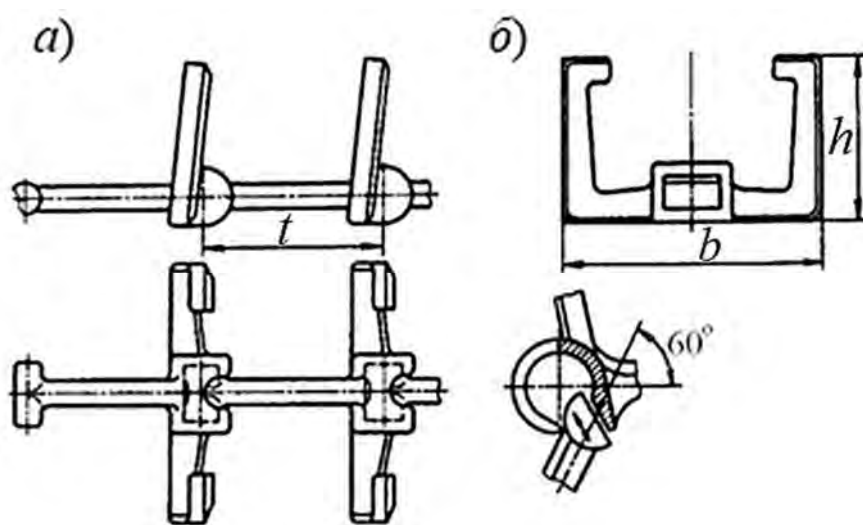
Литая разборная цепь из ковкого чугуна: *a* – конструкция; *б* – способ сборки-разборки
